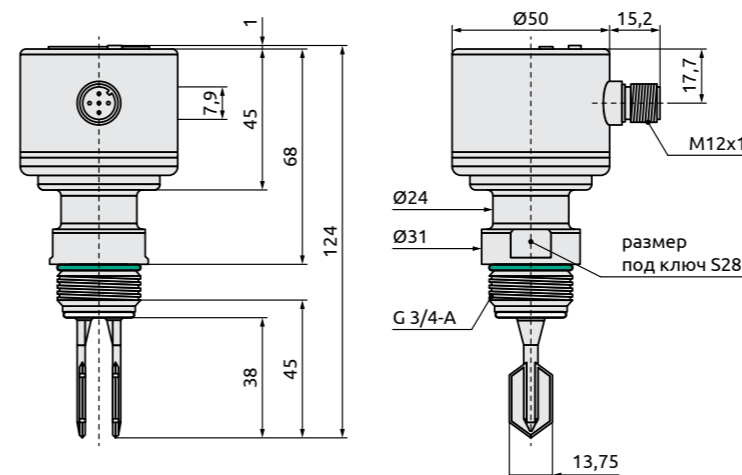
Габаритный чертеж вибрационного сигнализатора VLS-CS-T
